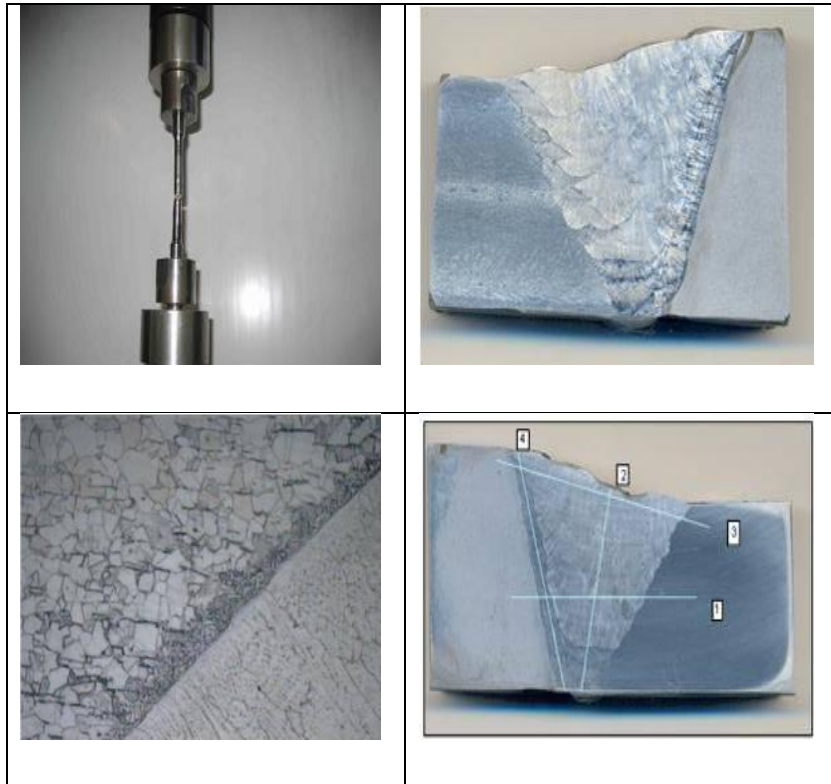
Aleaciones soldadura 82/182 de acuerdo al código ASME. ⁽³⁴⁾
